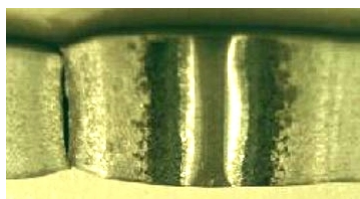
Пример разрушения сварного образца DP980 при растяжении
